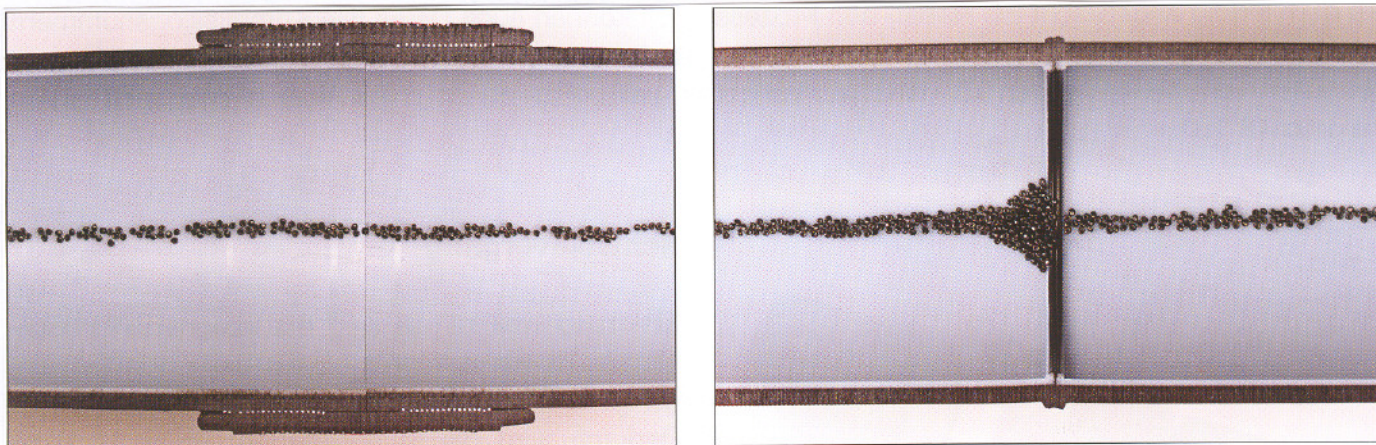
Сравнение методов электромуфтовой сварки (слева) и стыковой сварки (справа)
